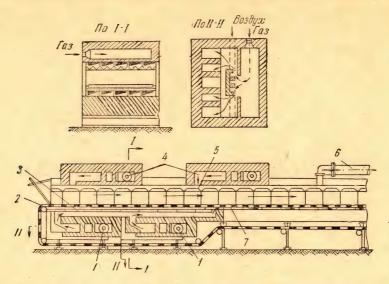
Схема переоборудования отжигательной печи на газовое топливо:
